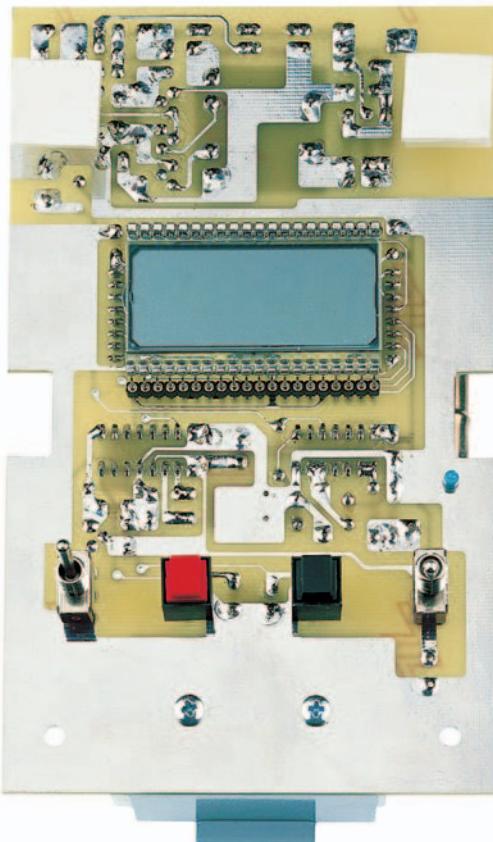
Photo d'un des prototypes de la platine du compteur Geiger EN1407, côté afficheur LCD, où sont également montés les deux poussoirs et les deux inverseurs.
